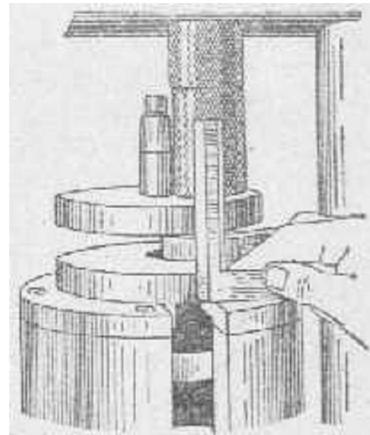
Напрессовка маховика с цапфой на шатунный палец
